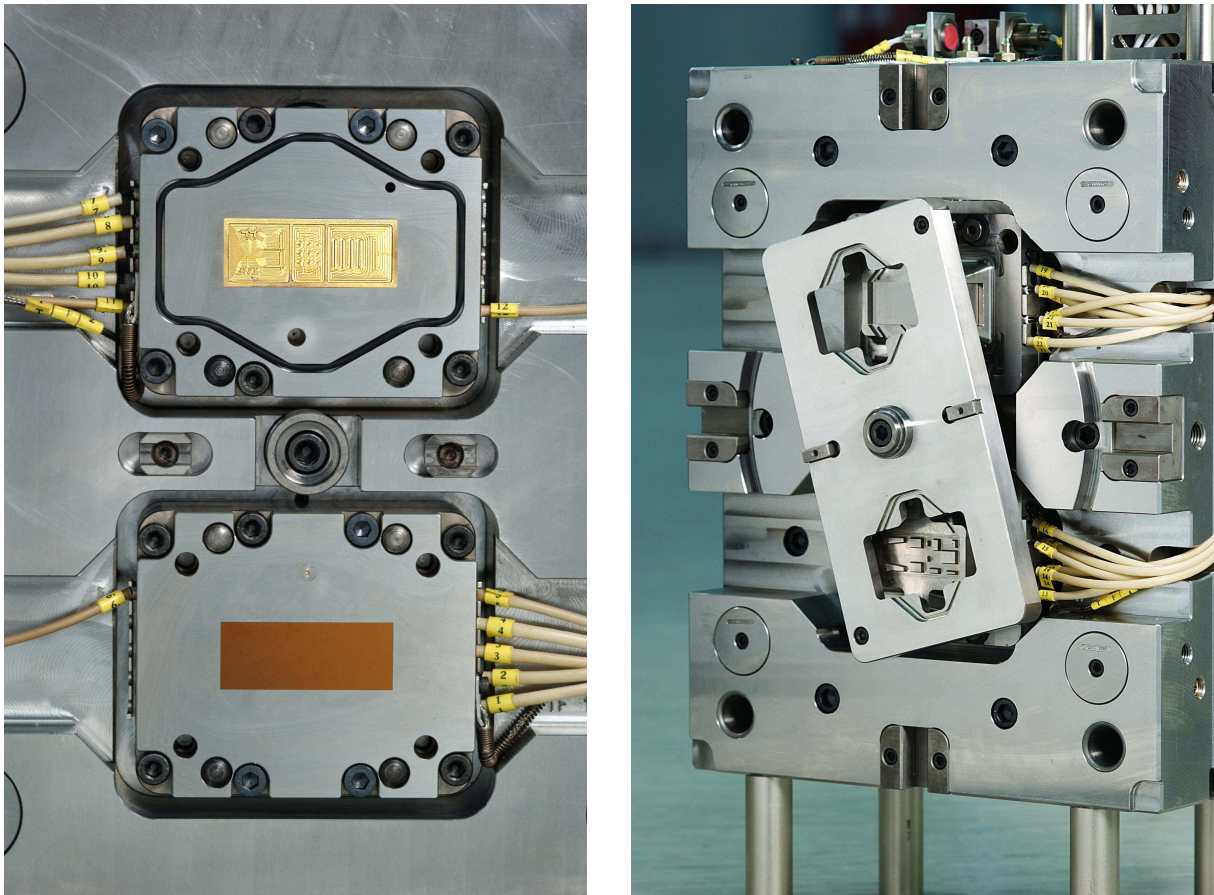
Aufsichten auf die beiden Werkzeughälften des 2K-Spritzgießwerkzeuges
